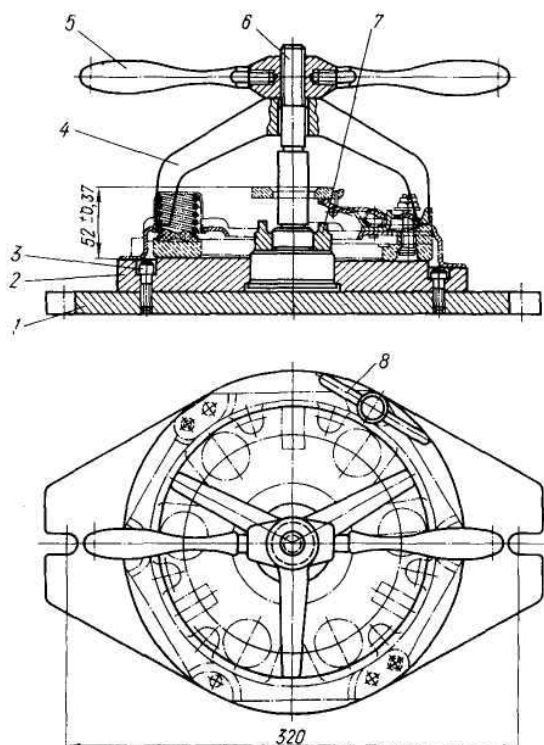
Приспособление для разборки и сборки ведущего диска сцепления:
